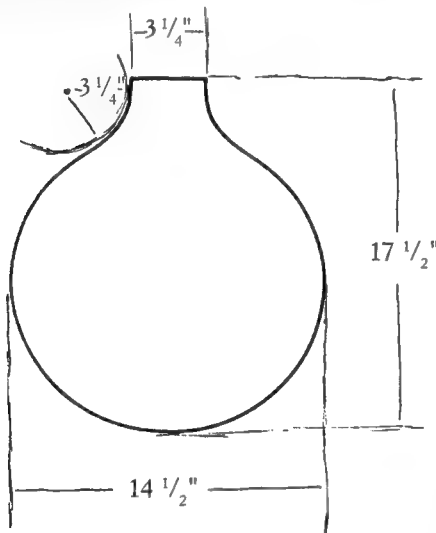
Die traditionelle Konstruktion des Deckenumrisses.
